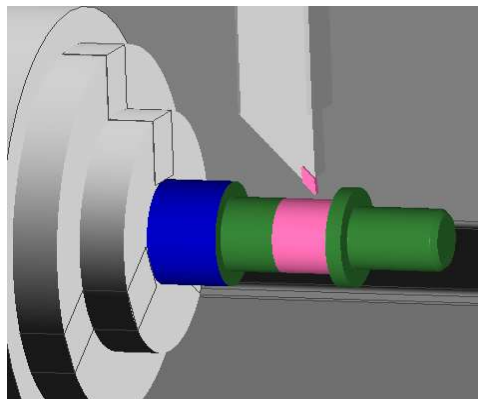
Hrubování  $\varnothing 28$  v EdgeCamu
